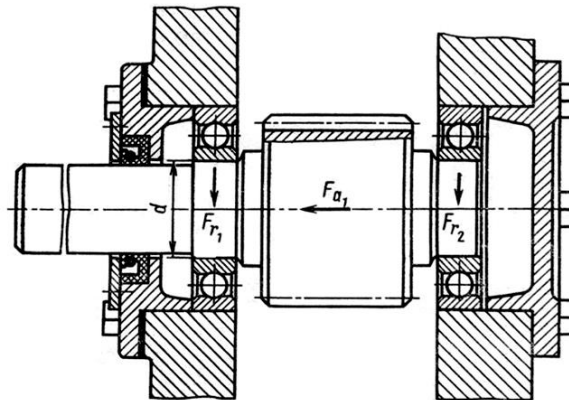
Подшипниковые узлы вала зубчатой передачи
